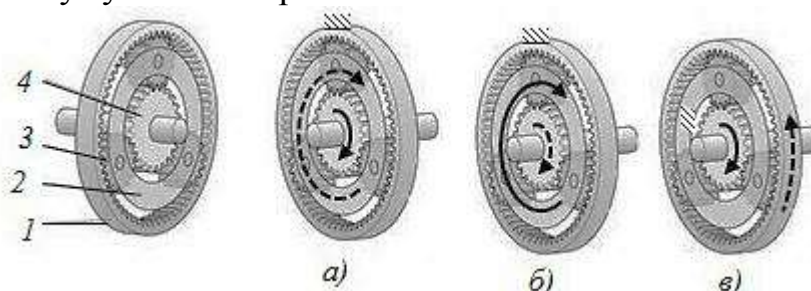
Схема планетарного механізму та випадки *передачі руху на різних передачах*: зменшувальної (а), збільшувальної (б) та передачі заднього ходу (в): 1 – коронна шестерня; 2 – водило; 3 – сателіти; 4 – сонячна шестерня
